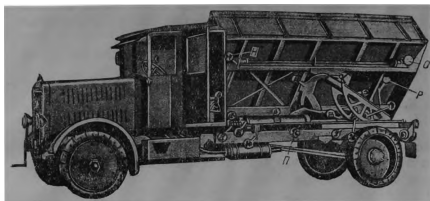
Наружное расположение рычага управления самосвалом Вуд.
